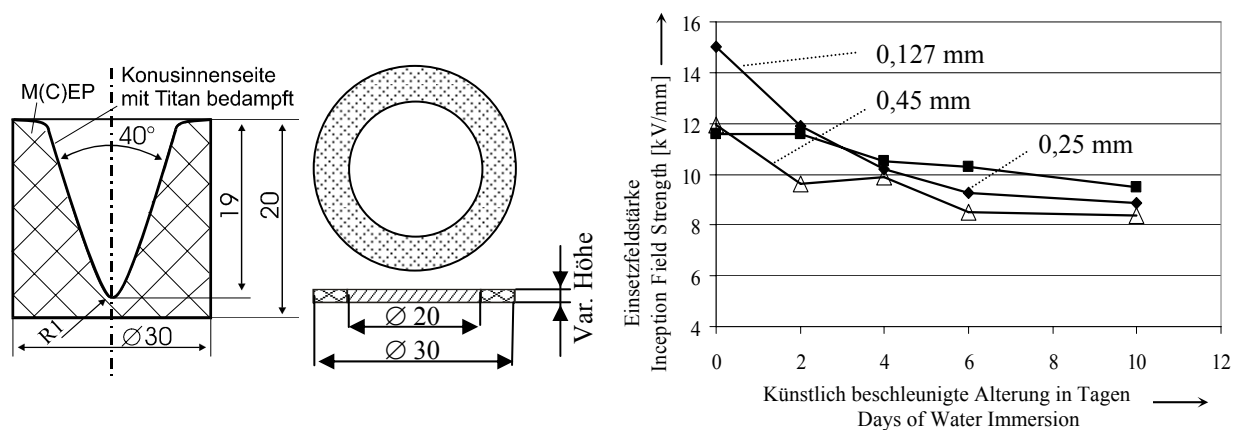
Kegelprüfkörper für TE-Messungen (links), Drauf- und Seitenansicht des Distanzringes (Polypropylen) mit variabler Höhe (Mitte); Verlauf der Einsetzfeldstärken während der Feuchtigkeitsalterung für die externen Mikrokavitäten (rechts)
